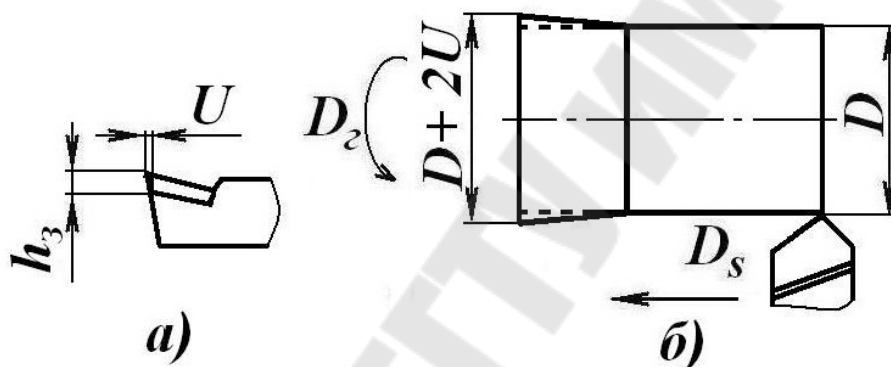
Изменение размеров обрабатываемой детали при наличии радиального размерного износа резца
